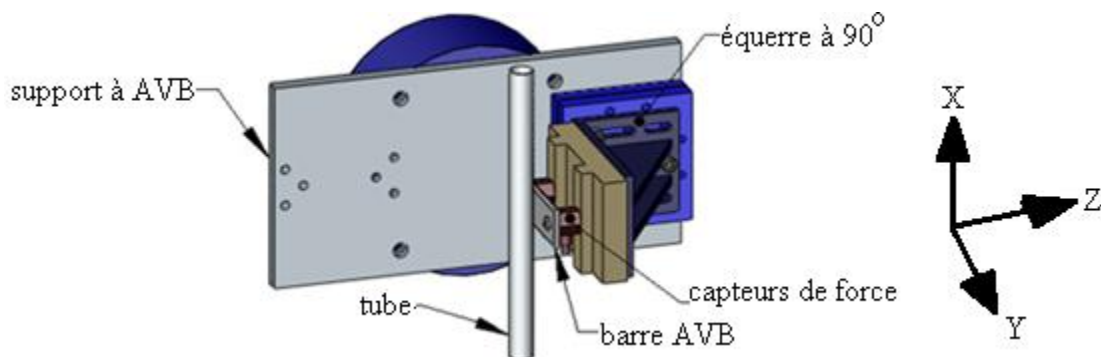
Assemblage de la coulisse de déplacement de la barre AVB.
